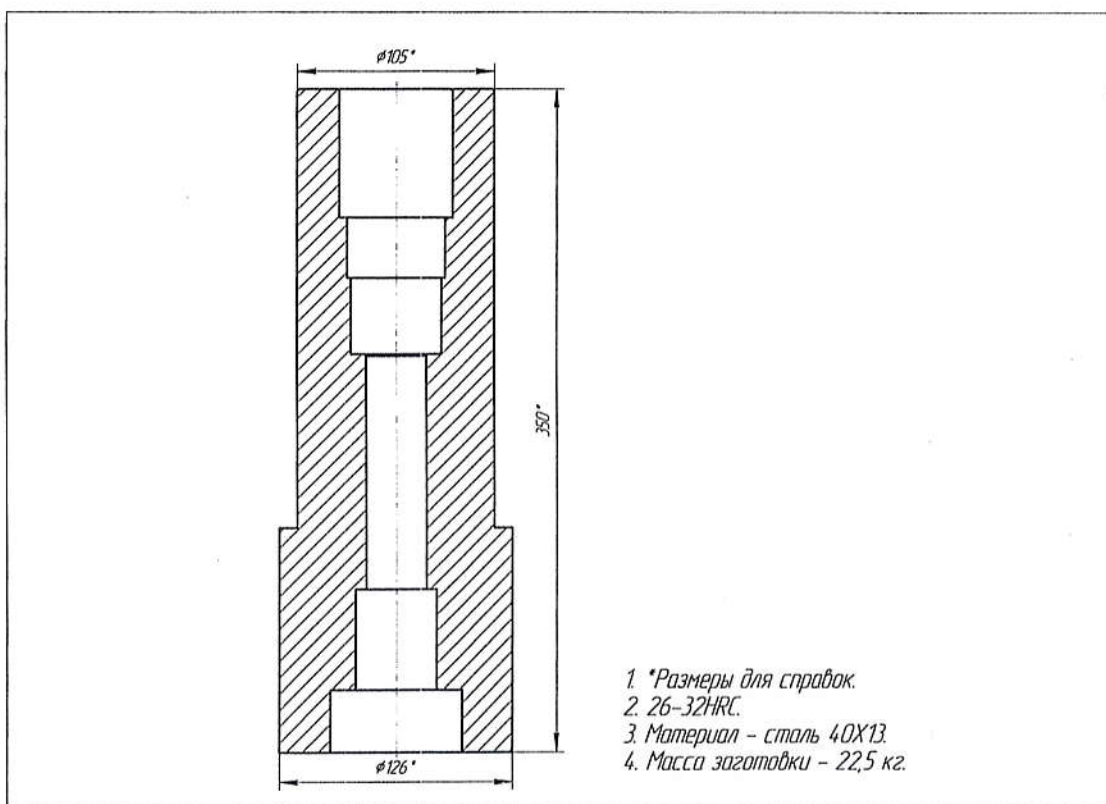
Эскиз детали головка ЭД129.02.001
